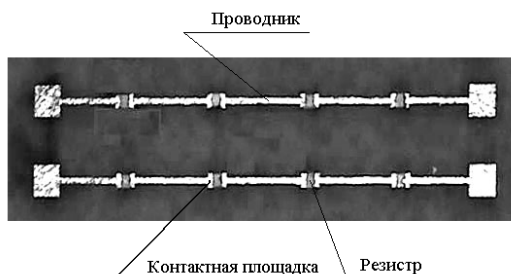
Внутренний монтаж резисторов. Опытный образец. Ширина проводника 0,5 мм.
